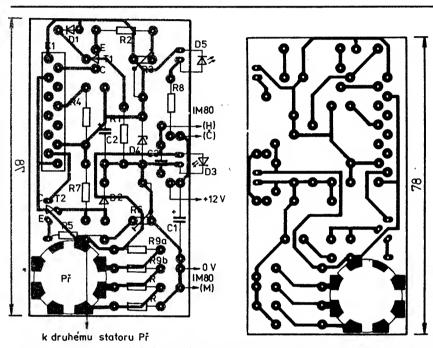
Obrazec plošných spojů kontaktní destičky (X23)
